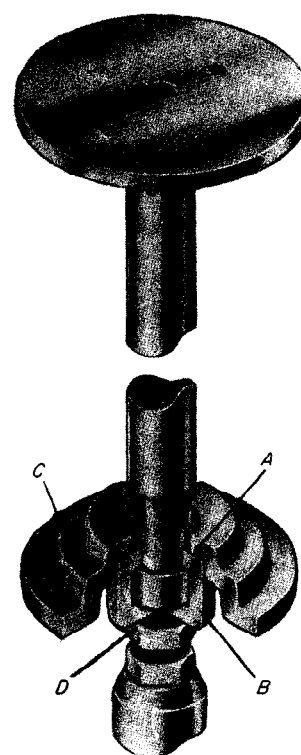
Construcción de un rotador libre: (A) Chavetas, (B) Copa, (C) Platillo, (D) Taqué (TRW Inc.).
